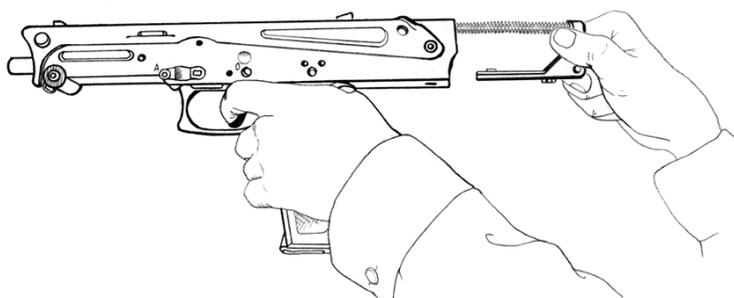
Постановка корпуса затыльника в коробку автоматики
